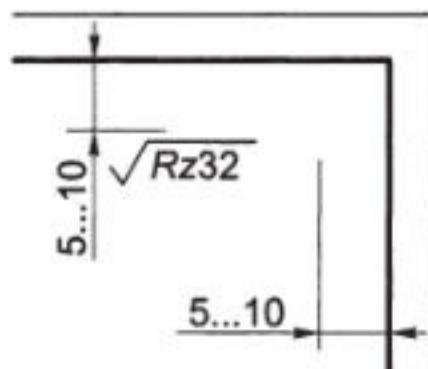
Обозначение шероховатости, одинаковой для всех поверхностей изделия
